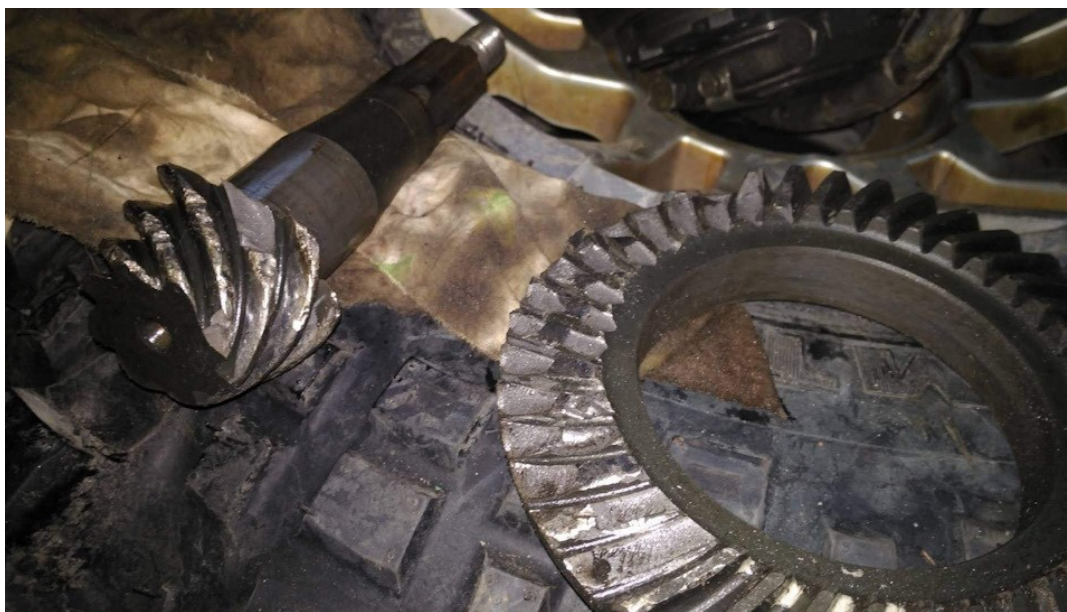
Разрушение ведущей и ведомой шестерни редуктора заднего моста
